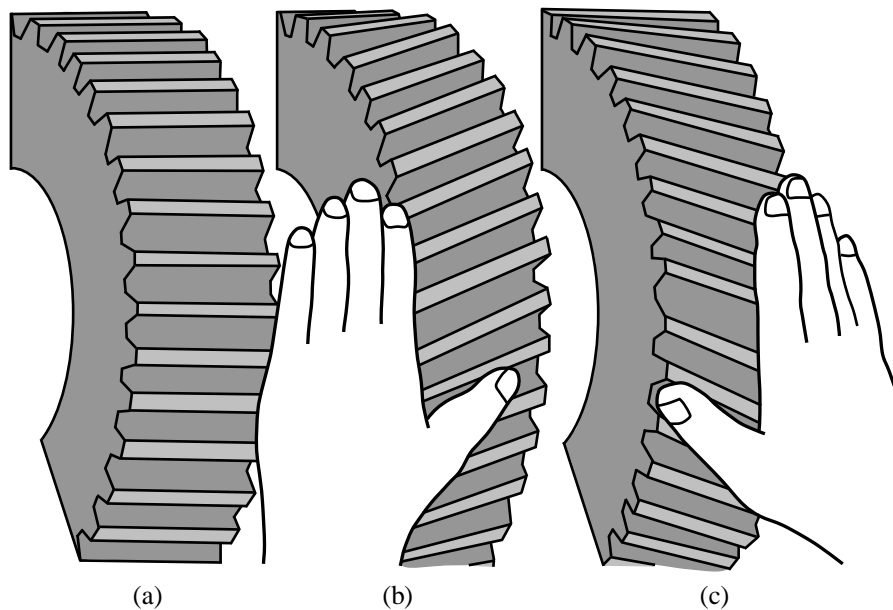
(a) Roda cilíndrica exterior de dentes retos; (b) Roda cilíndrica exterior helicoidal com hélice esquerda; (c) Roda cilíndrica exterior helicoidal com hélice direita.
